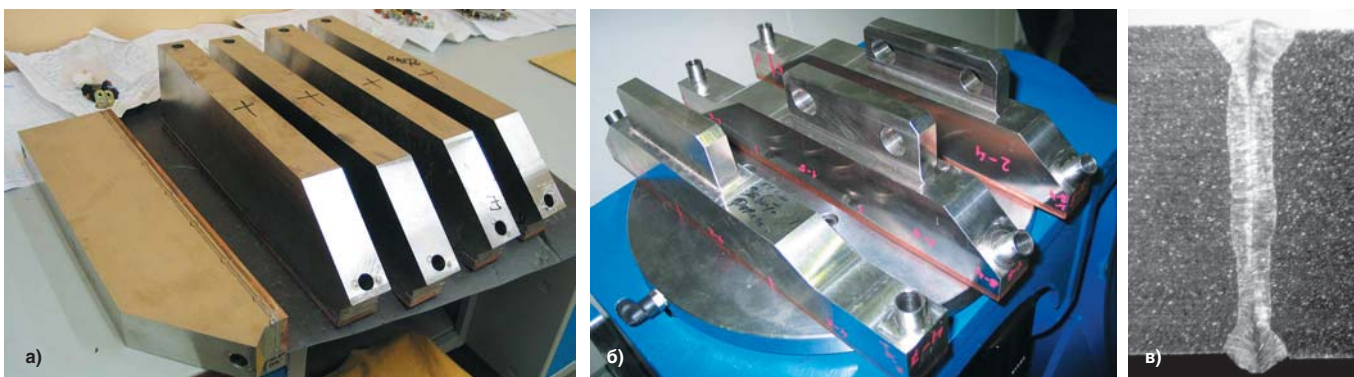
Корпусы отражающей мишени ЦСД из стали 316L: а) после лазерной сварки волоконным лазером, б) после механической обработки и рентгеновского контроля качества сварки, в) макрошлиф сварного шва толщиной 7 мм
